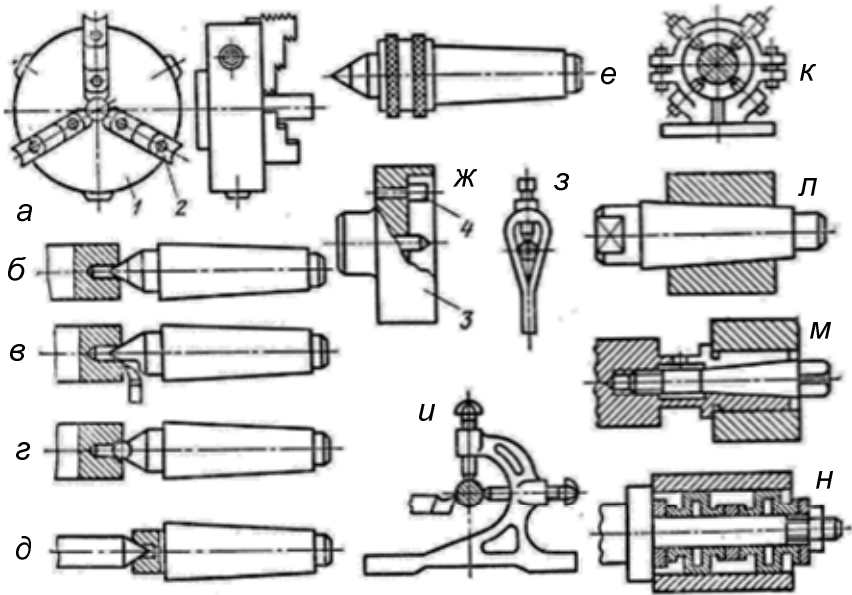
Способы закрепления заготовки на токарно-винторезных станках: *а* – патрон (самоцентрирующий или несамосцентрирующий); *б* – упорный центр; *в* – срезанный центр; *г* – центр со сферической рабочей частью; *д, е* – вращающиеся центры; *ж* – поводковый патрон; *з* – хомутик; *и, к* – люнеты; *л* – коническая оправка; *м* – цанговая оправка; *н* – упругая оправка.
